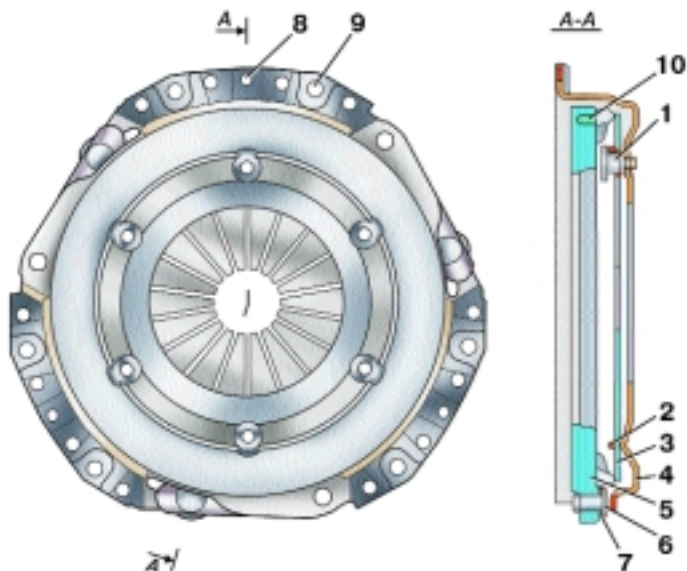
Нажимной диск сцепления «Лук» с кожухом в сборе: 1 – палец; 2 – опорное кольцо; 3 – диафрагменная пружина; 4 – кожух сцепления; 5 – нажимной диск; 6 – заклепка; 7 – соединительная пластина; 8 – отверстия под установочные штифты; 9 – крепежные отверстия; 10 – балансирующее отверстие
